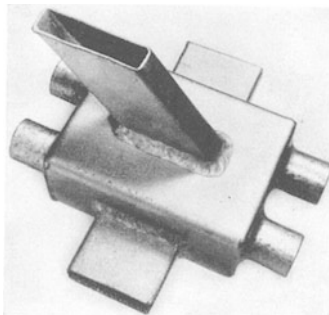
Geschweißter Kabelverteilerkasten aus 1,5 mm-Al-Blech.
